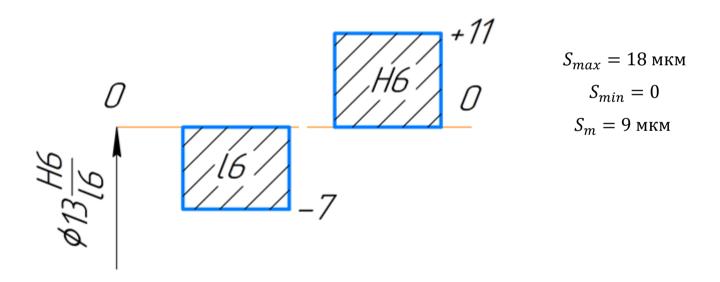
Посадка вешнего кольца шарикоподшипников с подшипниковой втулкой.
